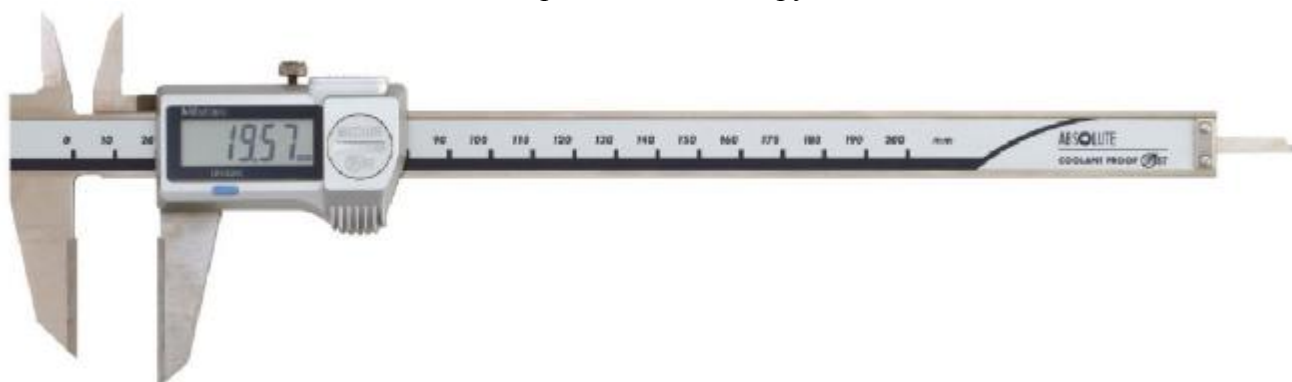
Общий вид штангенциркулей серии 573 модификации ABSOLUTE Digimatic разметочный с твердосплавными губками
